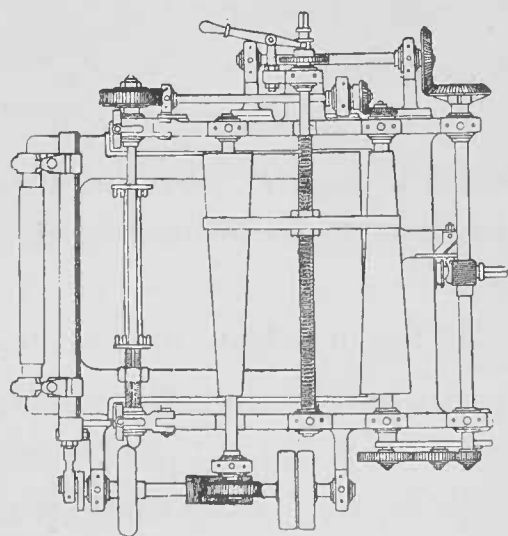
Machine à scier la feuille anglaise, système Le Blanc (plan).
